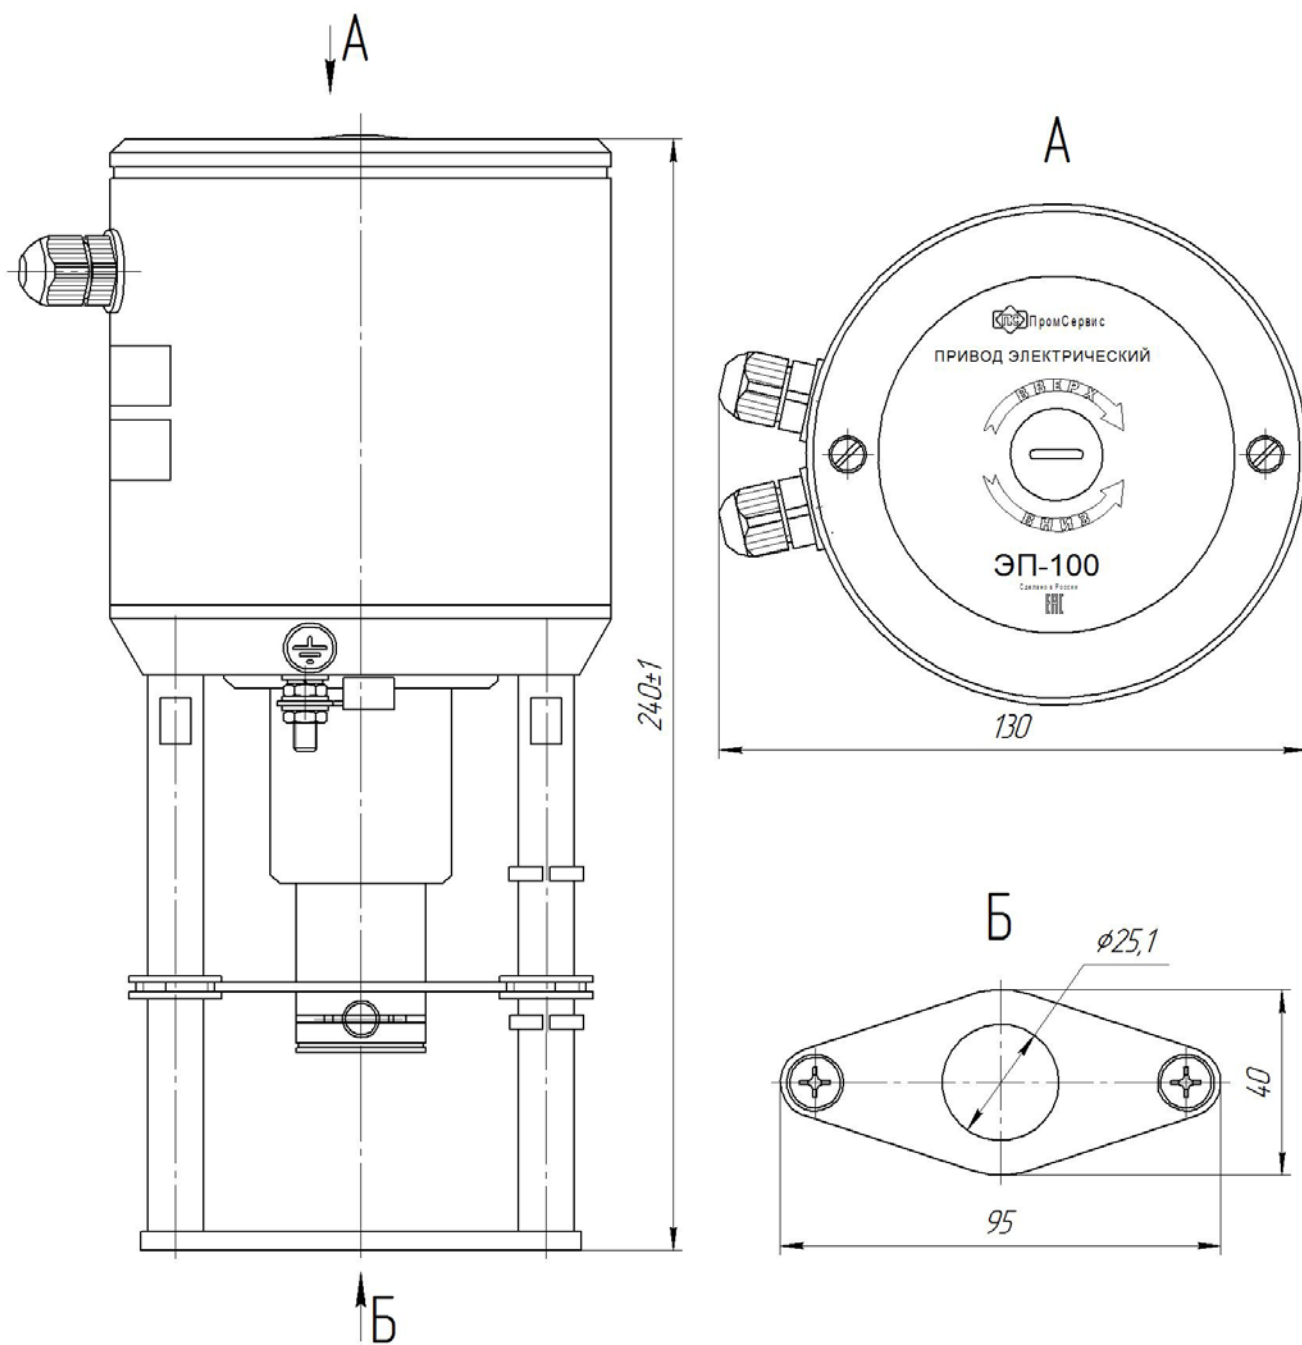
Габаритные и присоединительные размеры привода исполнения ЭП-100-03/2
